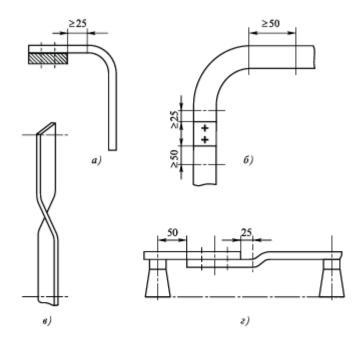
Виды изгибов шин: a — на плоскость; δ — на ребро; θ — «штопором»; ε — «уткой»
